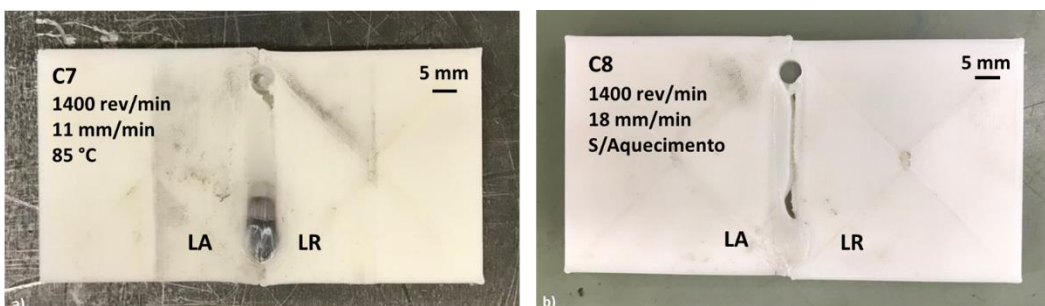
Aspeto visual da superfície das placas soldadas com combinação de parâmetros 7 e 8.
